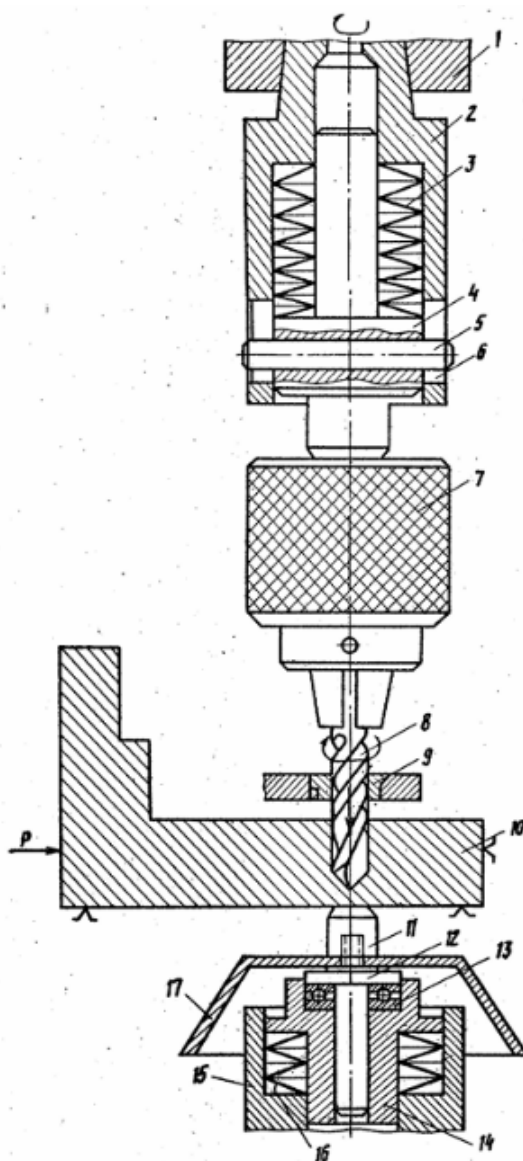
Пристрій для свердління наскрізних отворів з підпорною п'яткою
